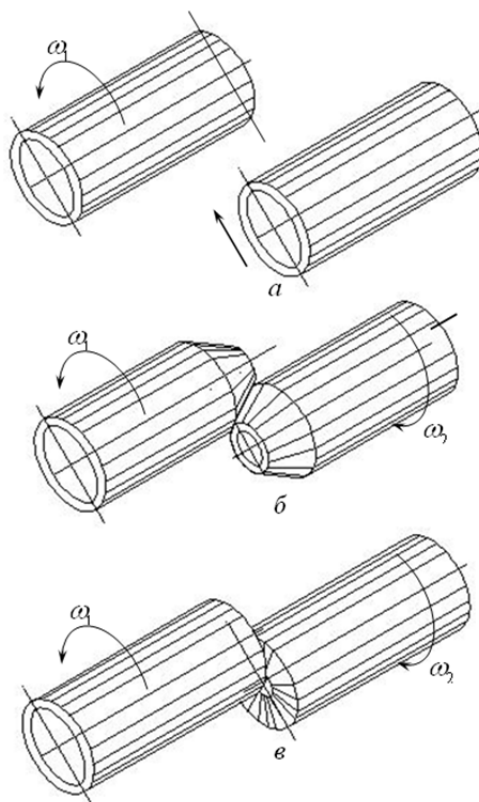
Получение плоских дниц при взаимной обкатке трубчатых заготовок:
